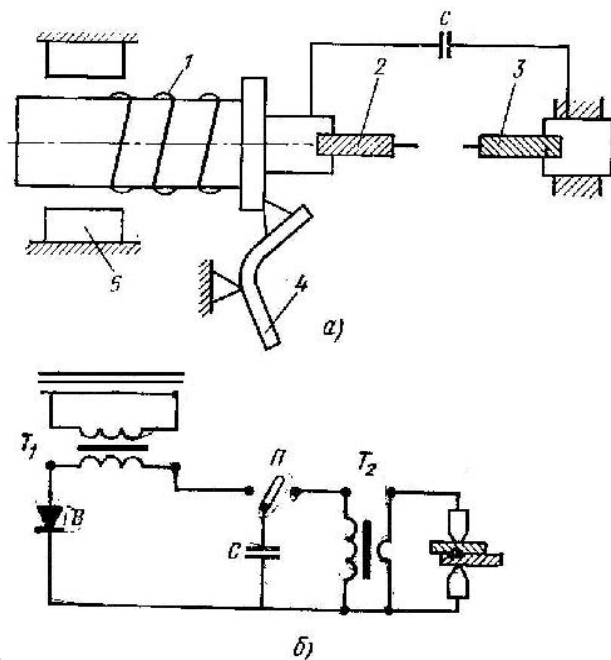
Схемы конденсаторной сварки: а) с подачей тока непосредственно от конденсатора на свариваемые заготовки: 1 – пружина, 2, 3 – свариваемые заготовки, 4 – защелка, 5 – направляющие; б) с подачей тока от конденсатора на первичную обмотку сварочного конденсатора: Т1 – повышающий трансформатор, Т2 – сварочный трансформатор В – выпрямитель, П – переключатель, С – конденсаторная батарея
